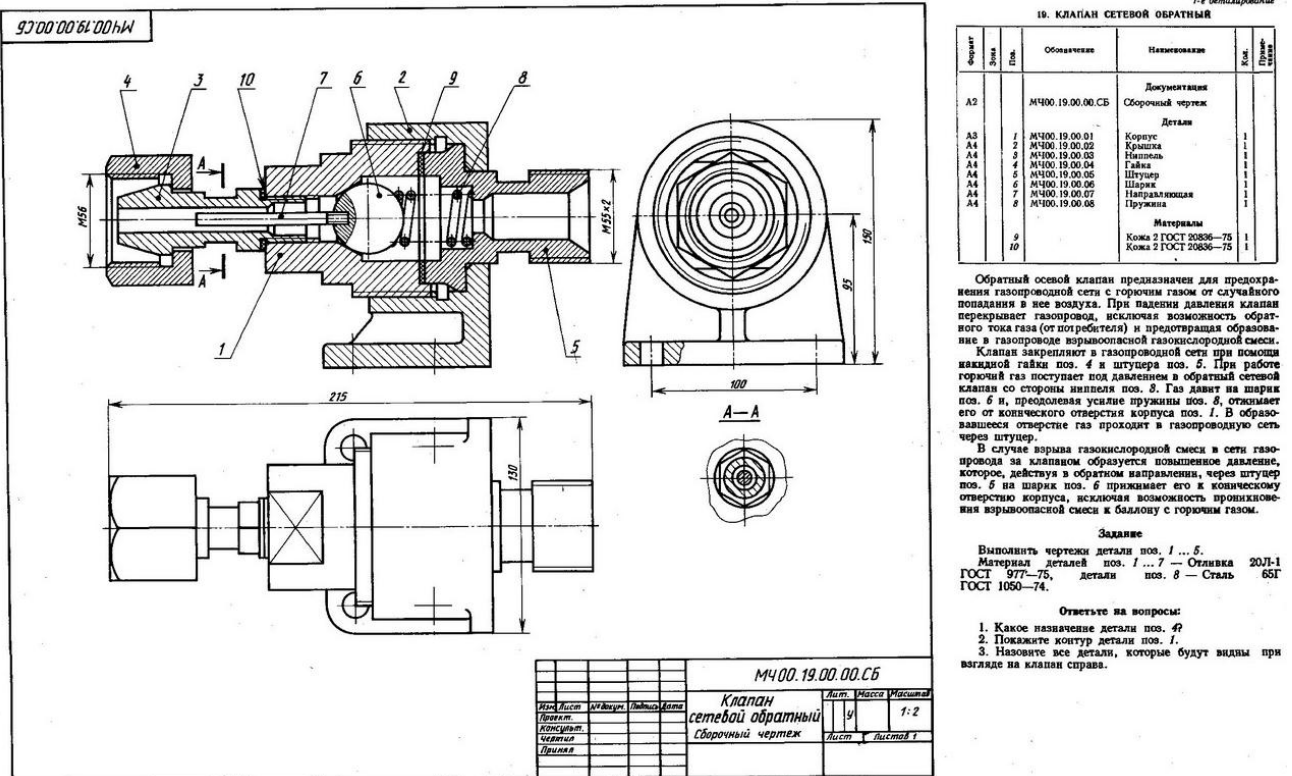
Вариант сборочного чертежа для моделирования.
